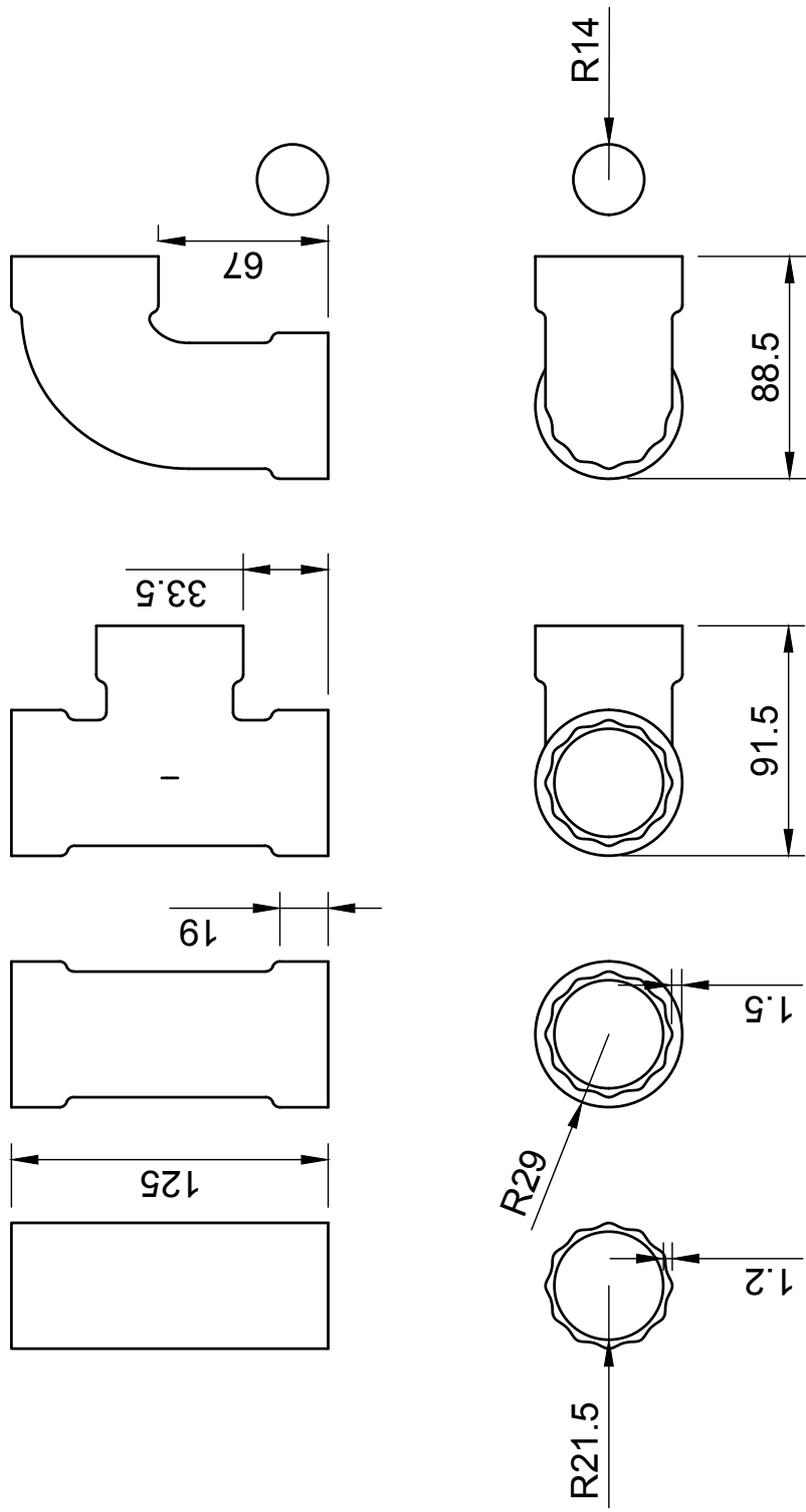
Desenho Técnico de conjunto GRICKS. Realizado pela autora
